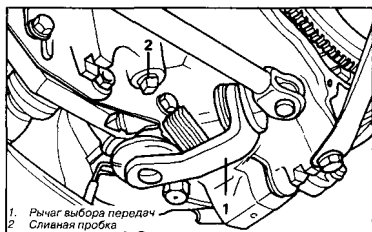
Рычаг механизма выбора передач и сливная пробка на коробке передач
